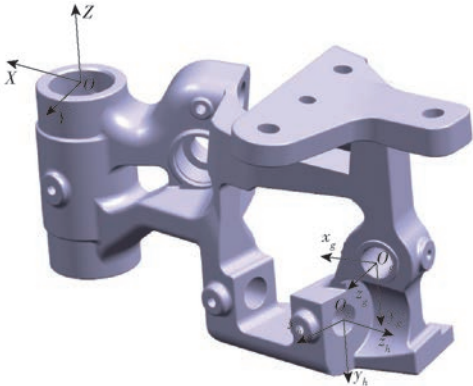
工件坐标系与夹绳盘轴孔的加工坐标系
